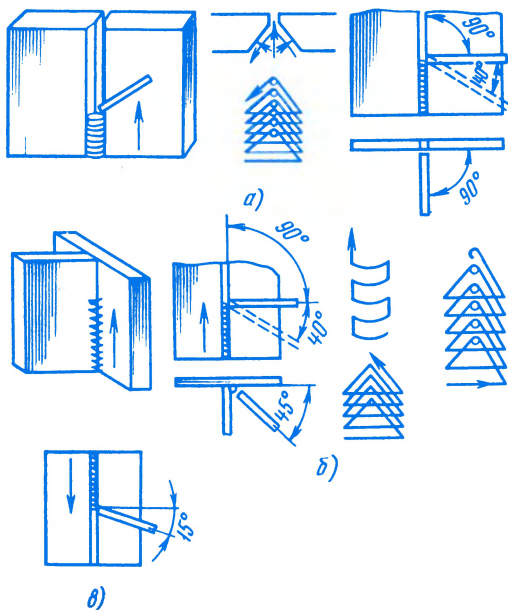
Положение и движения электрода при сварке в вертикальном положении:
